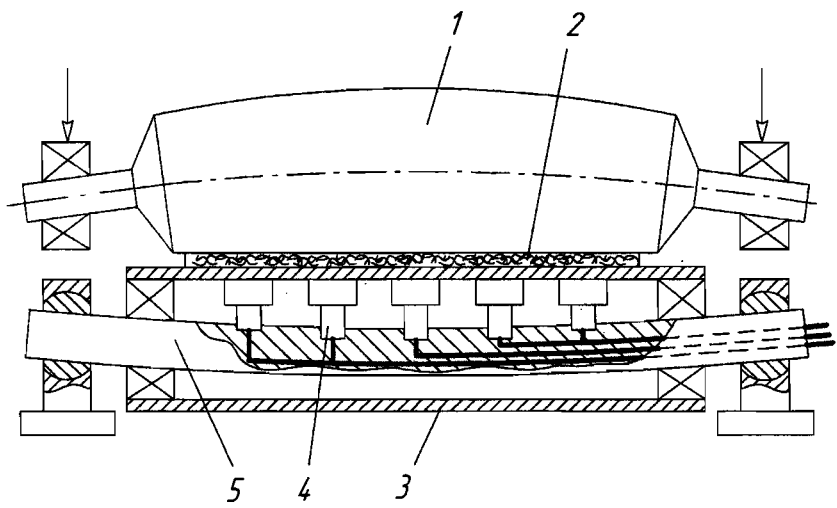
Схема прессы с валом Нипко: 1 – верхний вал прессы; 2 – бумажное полотно; 3 – рубашка вала Нипко; 4 – поршневой поддерживающий элемент; 5 - сердечник
